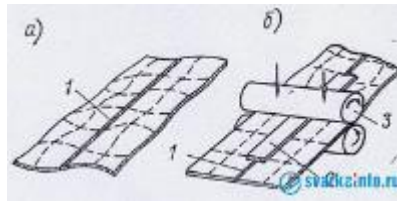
Схема исправления деформированных изделий из тонколистового металла а - листы после сварки до прокатки, б - схема процесса прокатки, 1 - сварной шов, 2 - накладка, 3 - прокатные валки
